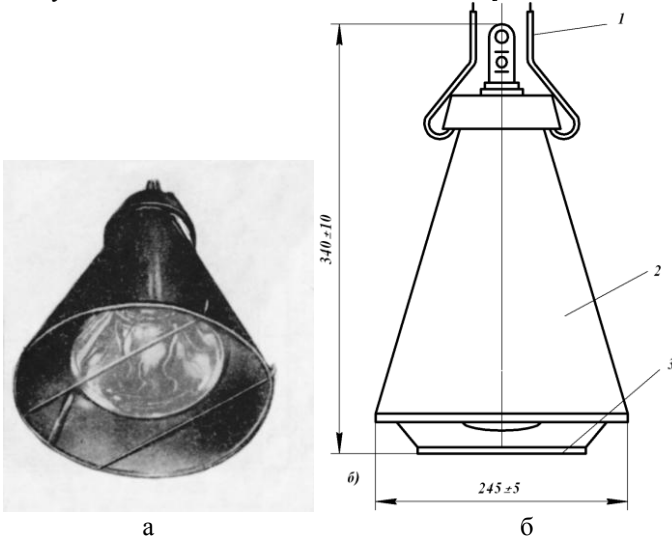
Інфрачервоний опромінювач типу ОРИ-1: а) загальний вигляд; б) схема конструкції: 1 – підвіска; 2 – корпус; 3 – сітка
